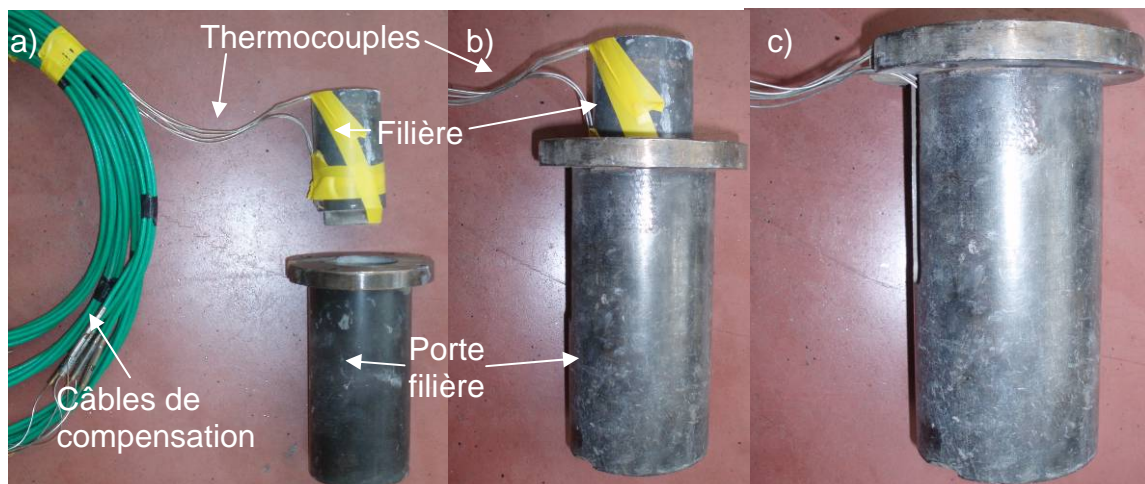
Photos de la filière percée et équipée des thermocouples K ; a) filière hors du porte filière c) filière assemblée dans le porte filière.
